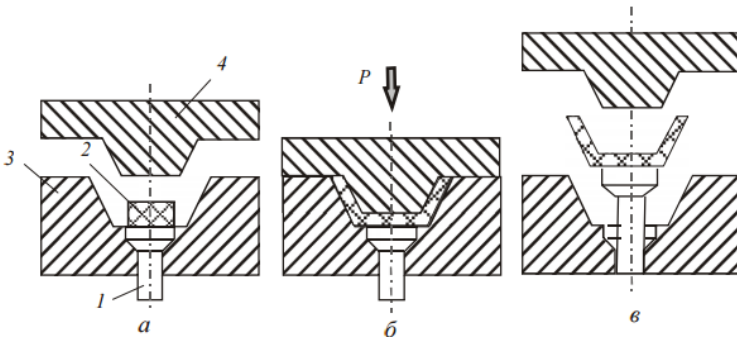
Схема компрессионного прессования реактопластов: а – загрузка пресс-материала; б – смыкание пресс-формы и прессование; в – раскрытие пресс-формы и извлечение изделия; 1 – выталкиватель; 2 – пресс-материал; 3 – пуансон; 4 – матрица
